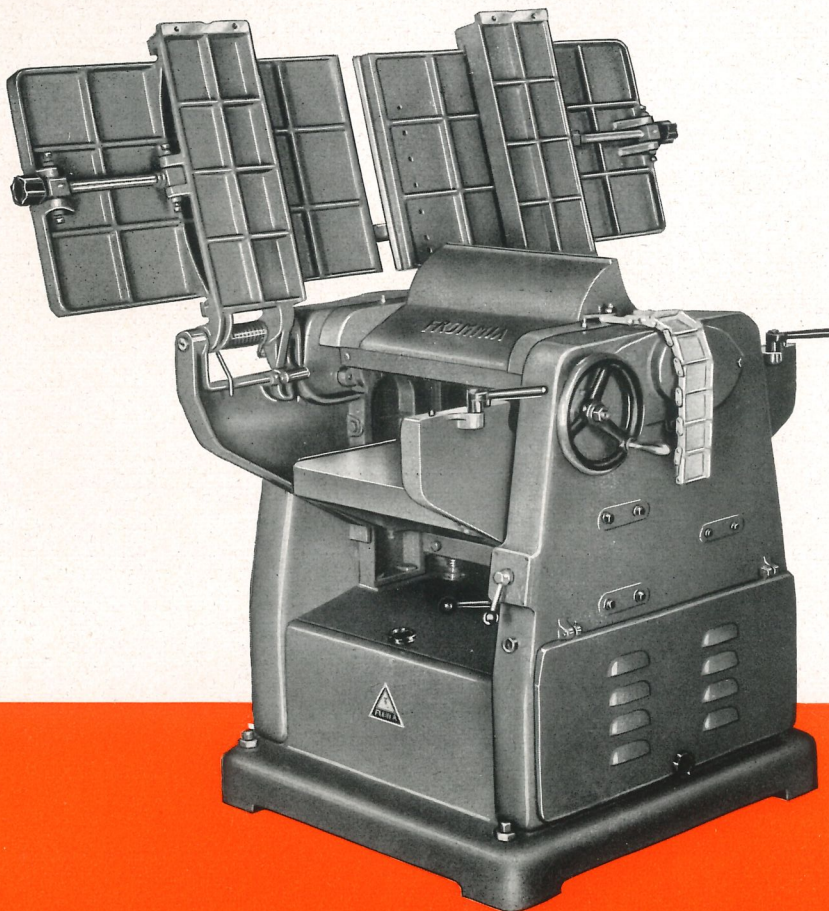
Type 260 K. Kombinierte Abricht-, Füge- und Dickenhobelmaschine mit hochgeklappten Abrichttischen.
